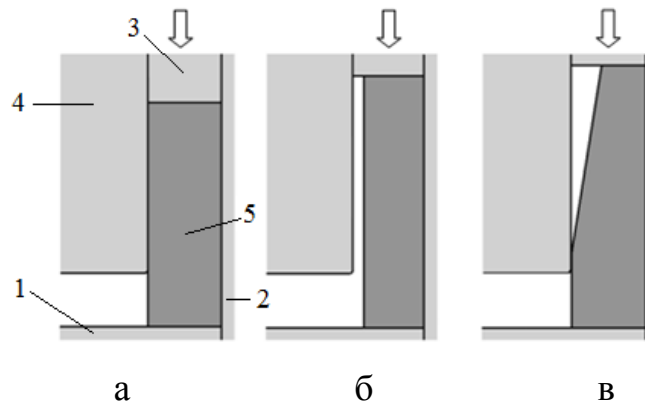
Розрахункова схема видавлювання заготовок різної форми: 1 - пуансон, 2 - матриця, 3 - контрпуансон, 4 - оправка, 5 - заготовка
